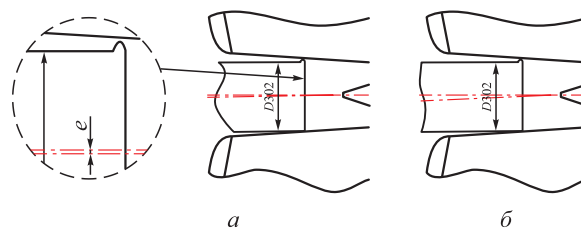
Отклонение заготовки от оси прокатки при первичном захвате: эксцентриситет осей заготовки и прокатки (а); угол наклона заготовки (б)
